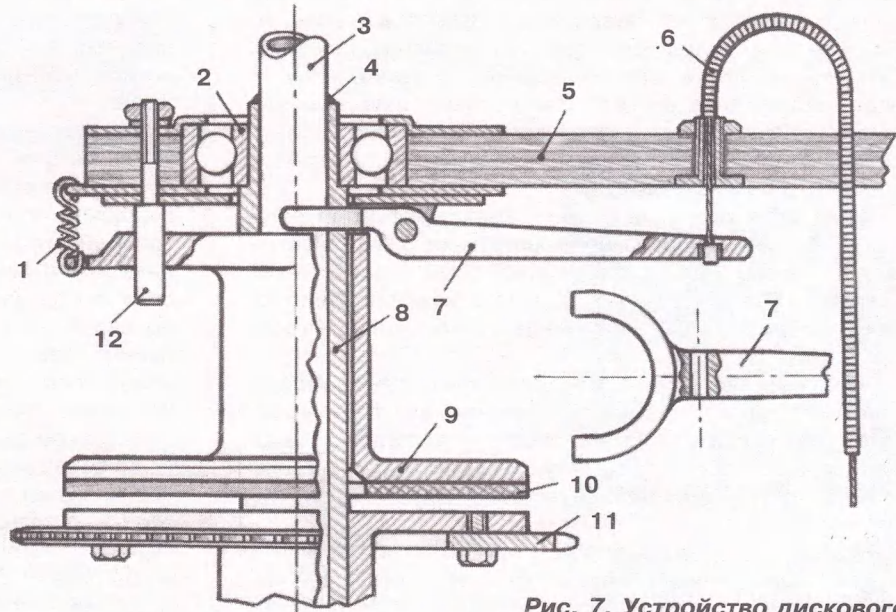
Устройство дискового тормоза: 1 — возвратная пружина; 2 — подшипник заднего моста; 3 — вал заднего моста; 4 — место сварки втулки; 5 — борт; 6 — трос; 7 — вилка привода дискового тормоза; 8 — втулка ведущего узла; 9 — шайба тормозного диска; 10 — фрикционный диск; 11 — ведомая звездочка; 12 — направляющие штыри (3 шт.).
